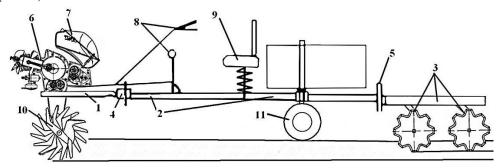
Общий вид малогабаритного почвообрабатывающего агрегата с фрезой и дисковой батареей: 1 — подмоторная рама; 2 — рама транспортного средства (прицеп); 3 — дисковая батарея; 4 и 5 — соединительные кронштейны; 6 — силовая установка; 7 — топливный бак; 8 — рычаги управления; 9 — сидение оператора; 10 — рабочий орган (фреза).
